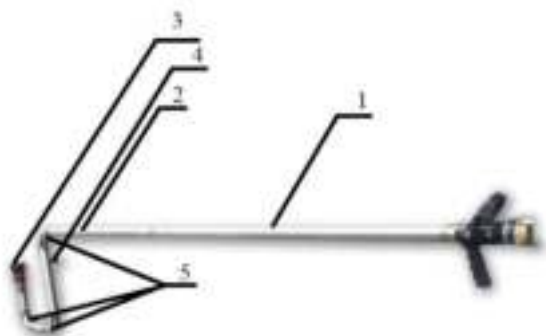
Конструктивные особенности ручного пожарного ствола
